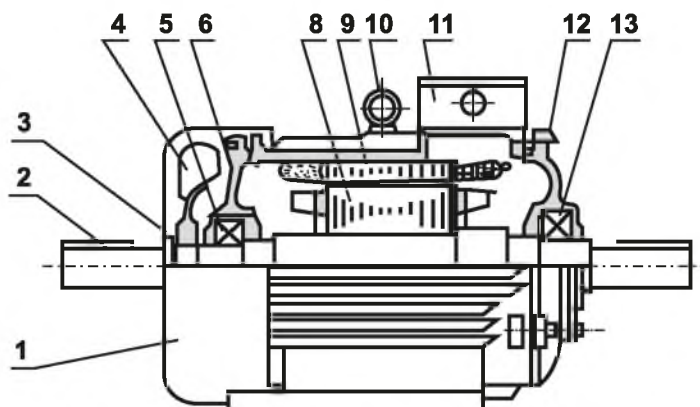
Конструкция электродвигателя с короткозамкнутым ротором
